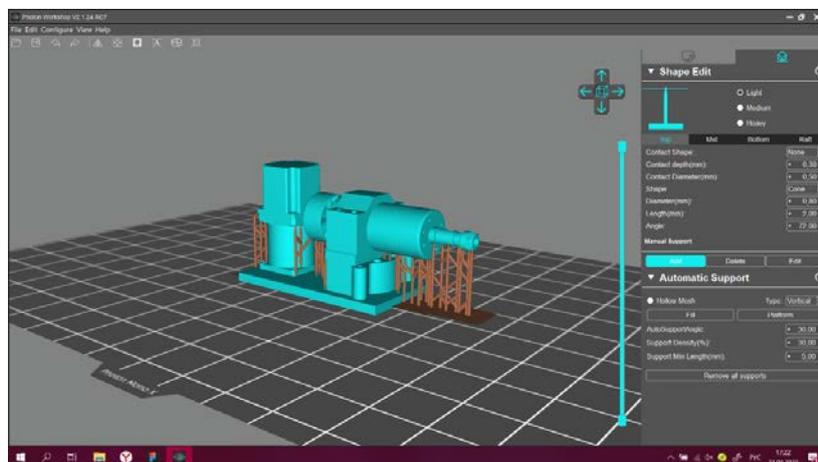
Подготовка детали к выращиванию на фотополимерном принтере
